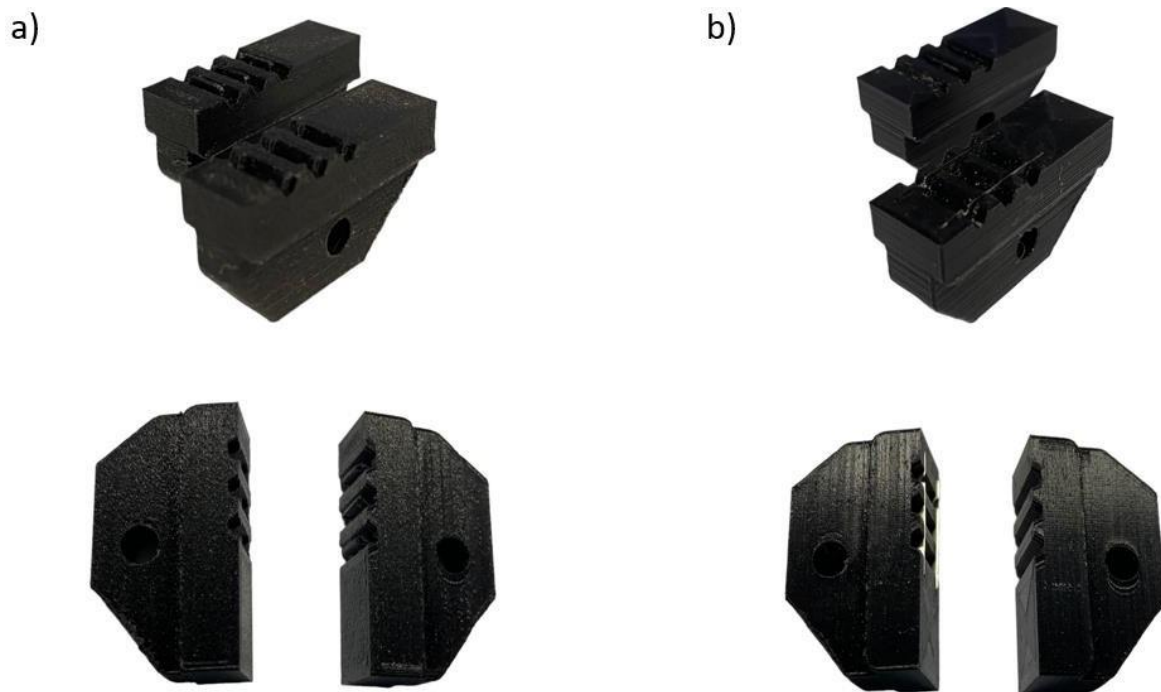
Prototipos de Molde pelacables a) Versión 1 b) Versión 2
